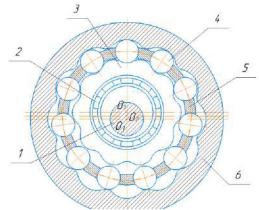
Схема передачи с ПТК с двумя циклоидальными колесами
